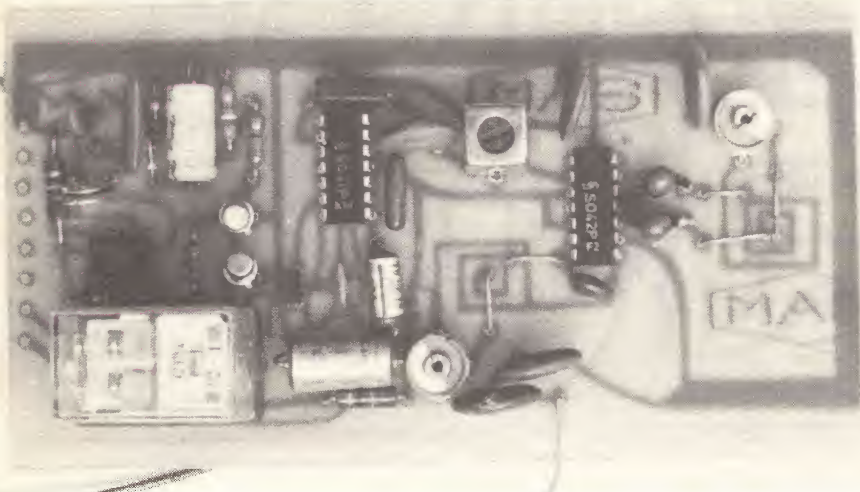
La piastra ricevente. L'uscita utilizzazione è collegata a una centrale d'allarme.
